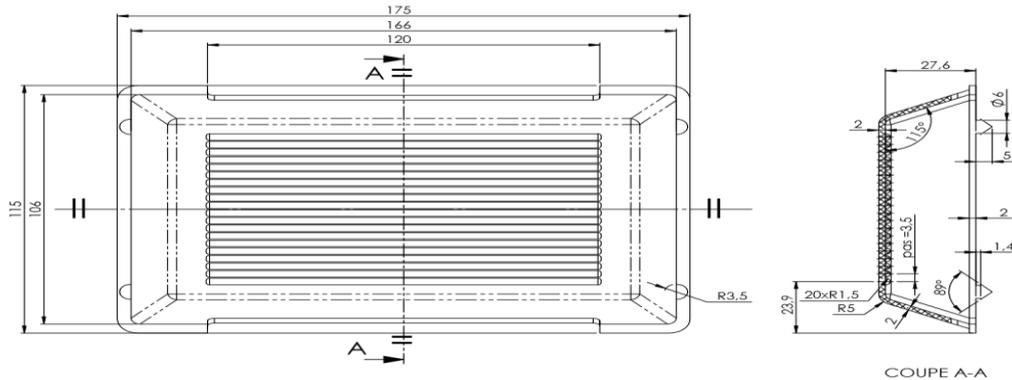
Les dimensions géométrique de la pièce (voir la mise en plan)
